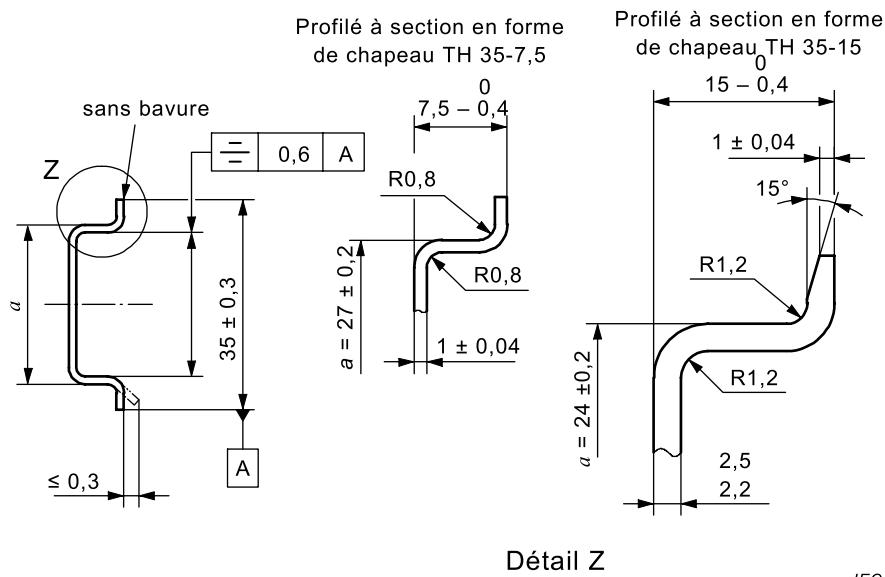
Profilés à section en forme de chapeau de largeur 35 mm pour fixation d'équipements par encliquetage
